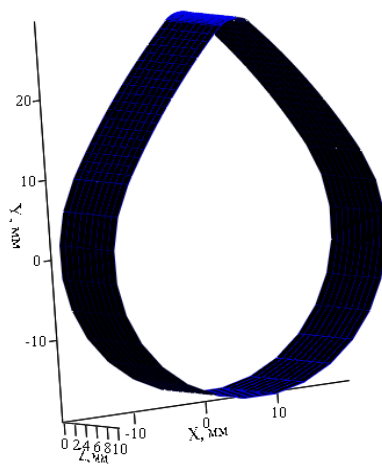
3D-модель поверхні кулачка розподільчого вала
